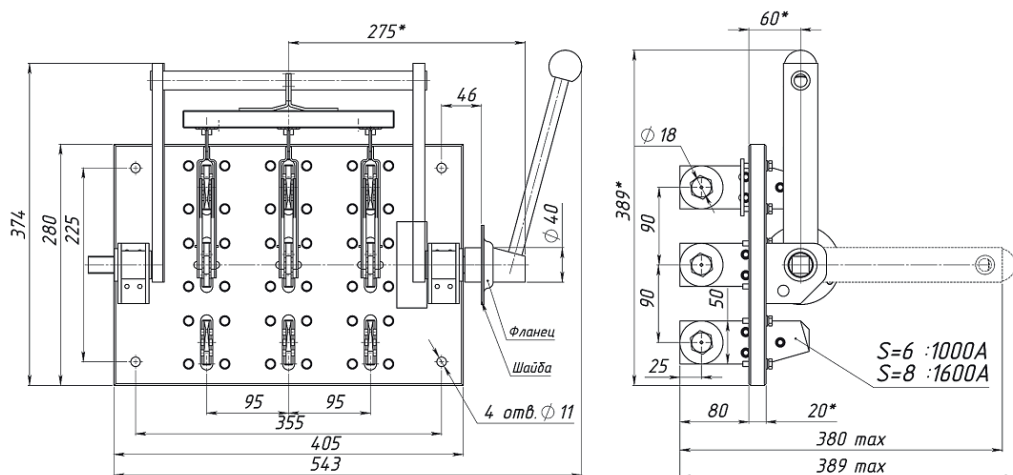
Разъединитель РЕ19-41(43)-72250-00 УХЛ3 на два направления с боковой смещенной рукояткой
